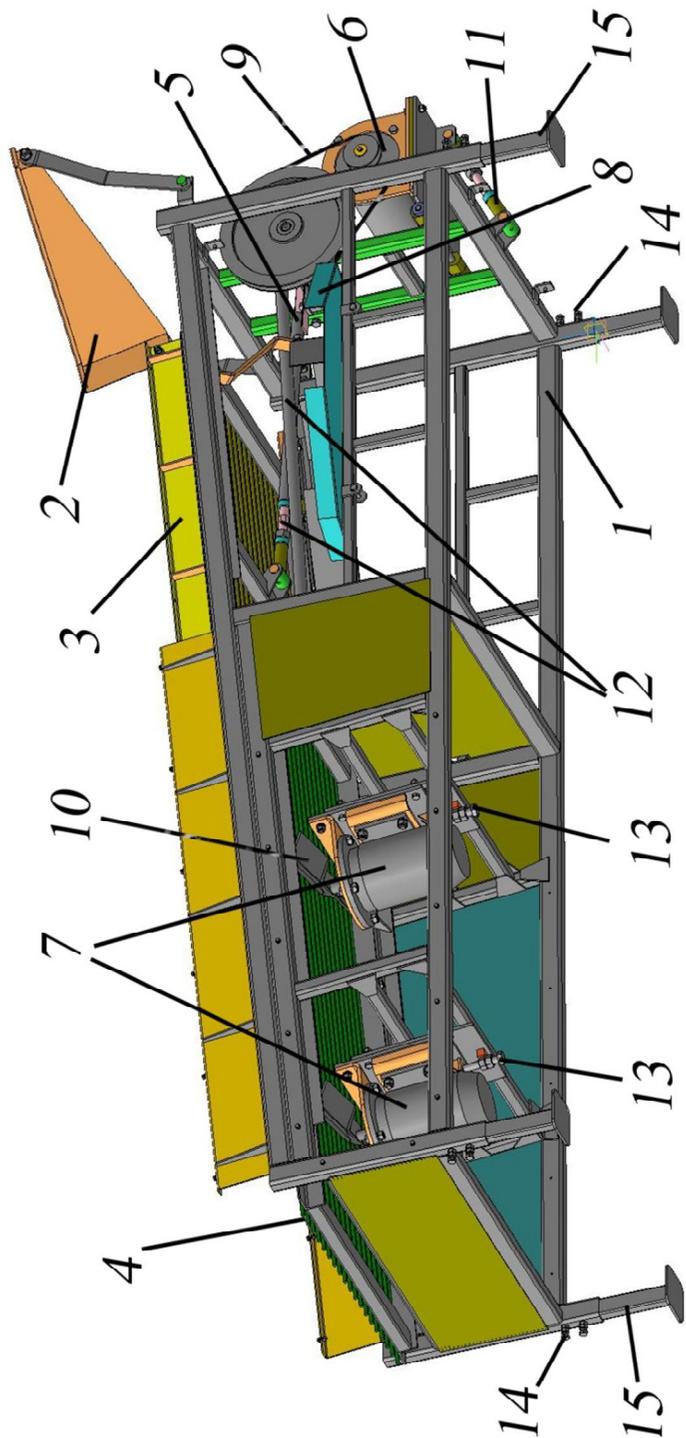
Общий вид машины для обрезки лука МОЛ-2
